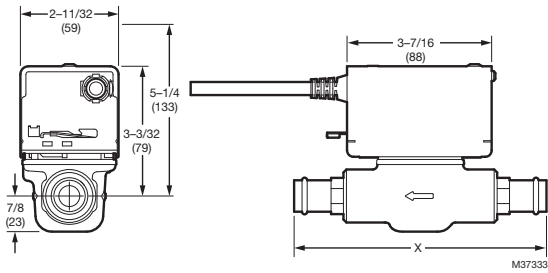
Dimensions (V8043A, V8043E). Mesures en po (mm). Voir le Table 1.
